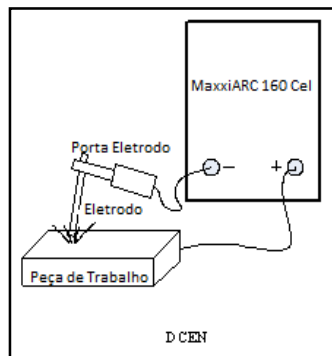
Conexão negativa para soldagem com eletrodo revestido
